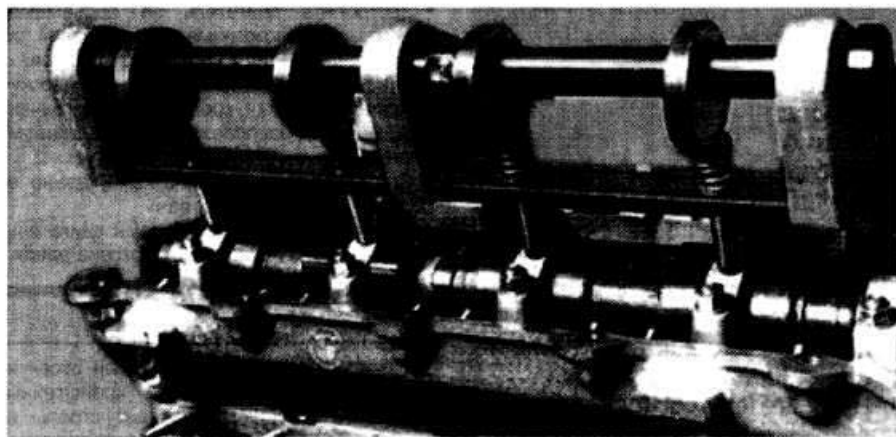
Приспособление BMW 11 32 60 для снятия и установки распределительных валов
